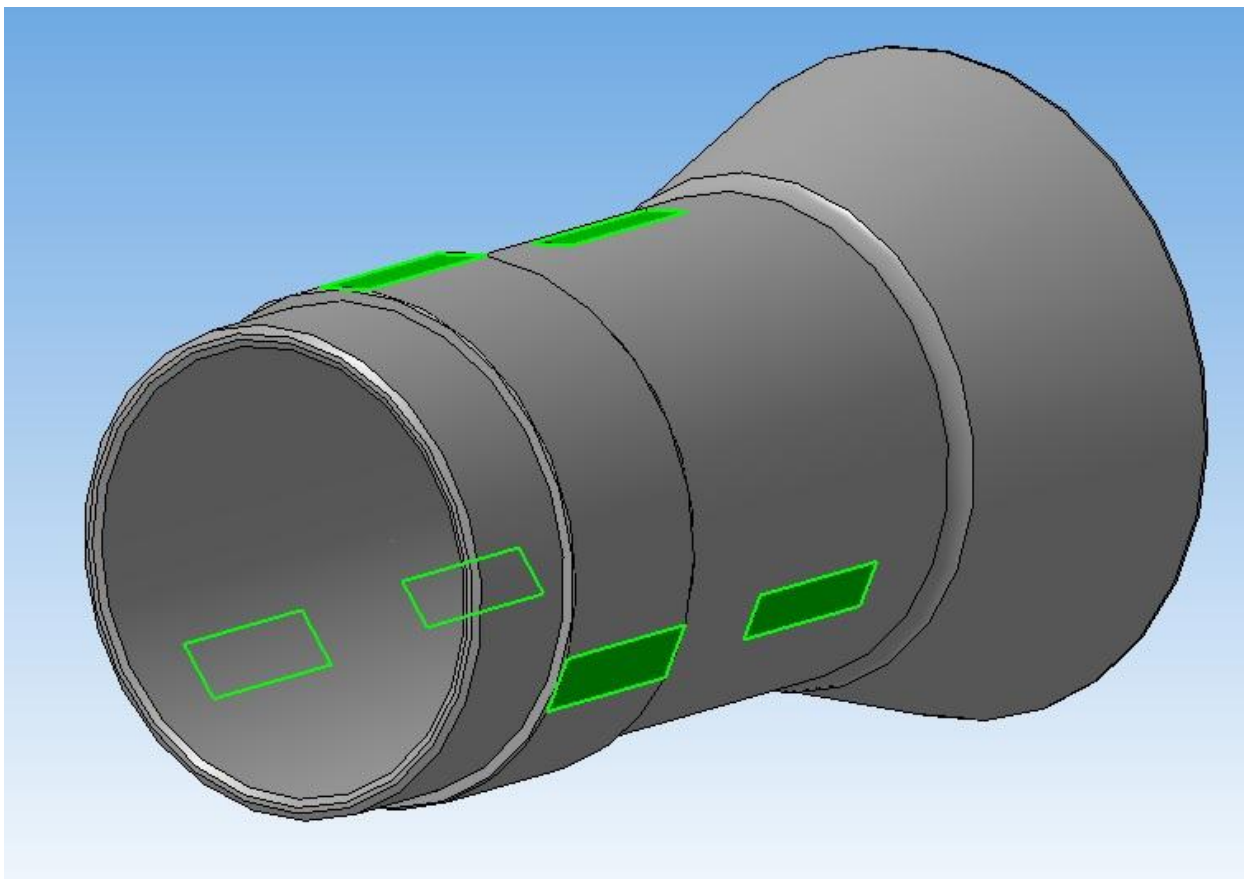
Поверхности (места) закрепления заготовки
